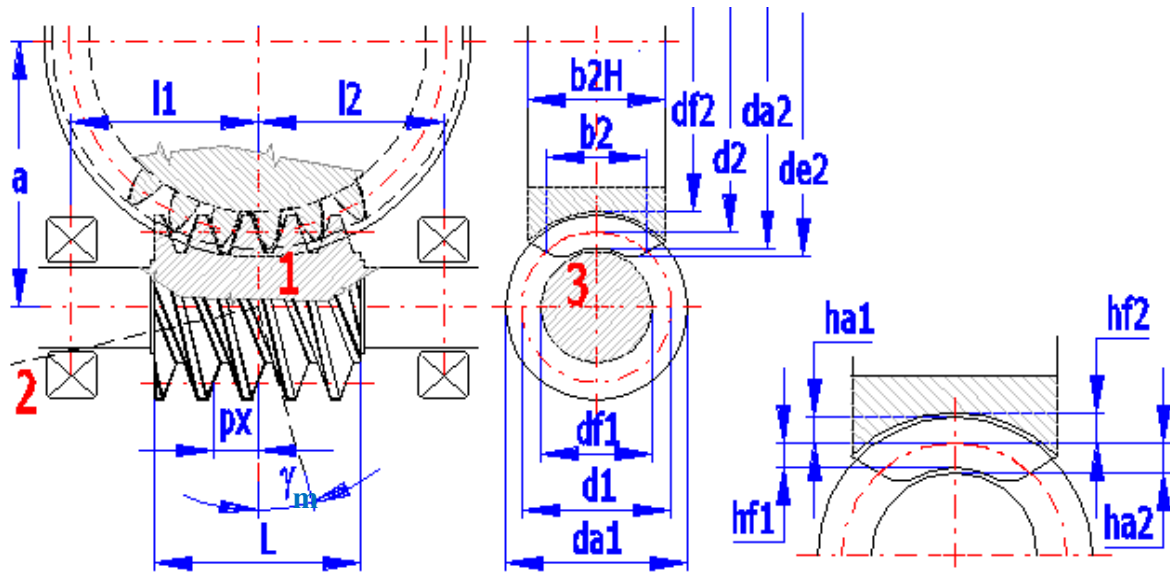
Dimensões de um parafuso sem-fim e roda-de-coroa
